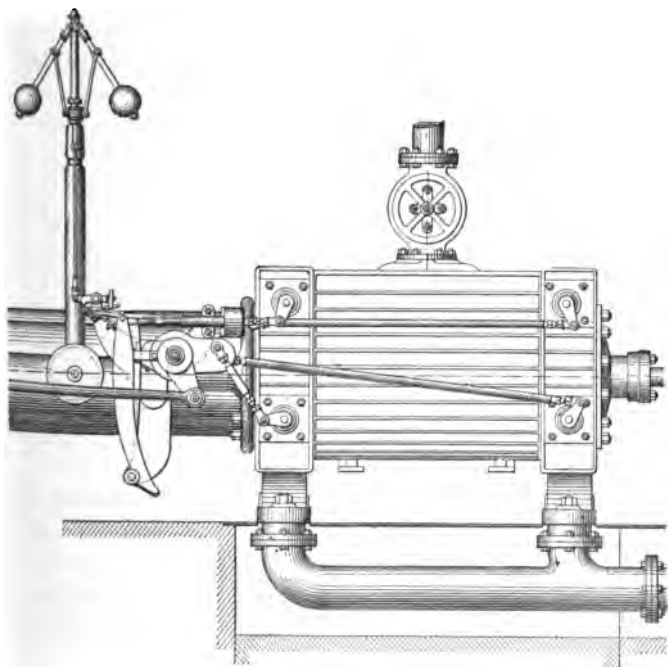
Machine Corliss à ressorts *en lame de sabre*, construite par E. Garnier.
